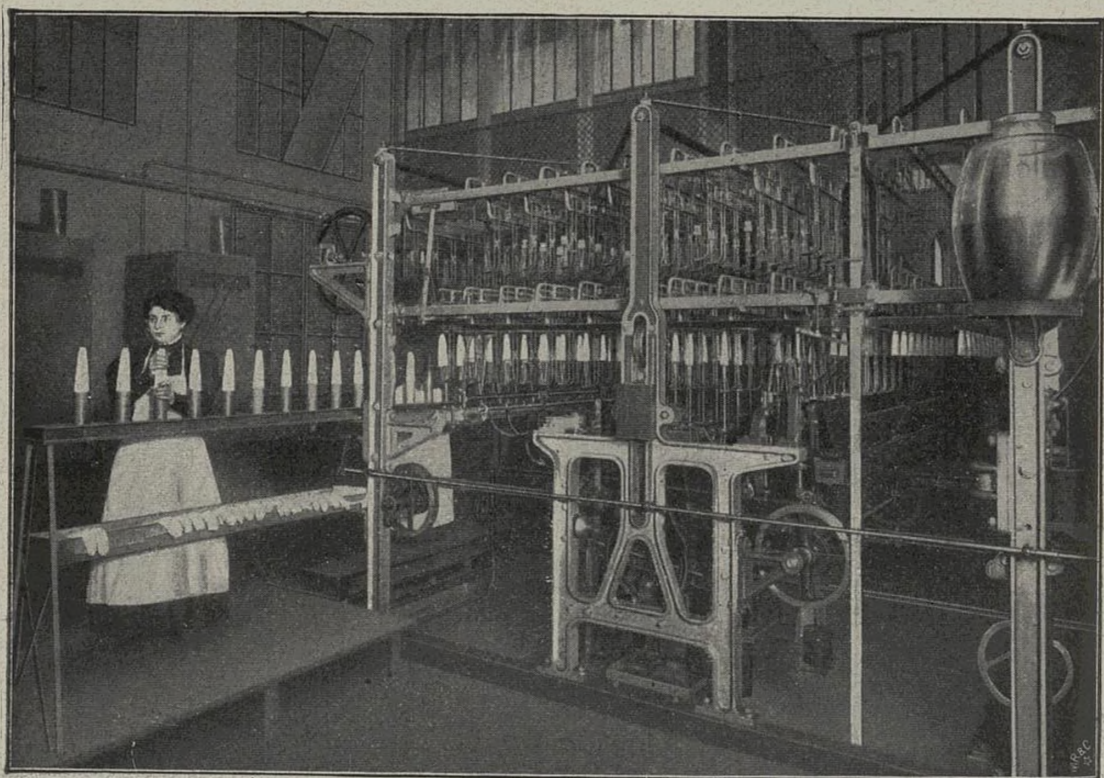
Opérations avant collodage. (Machine Muller et Bonnet.)
